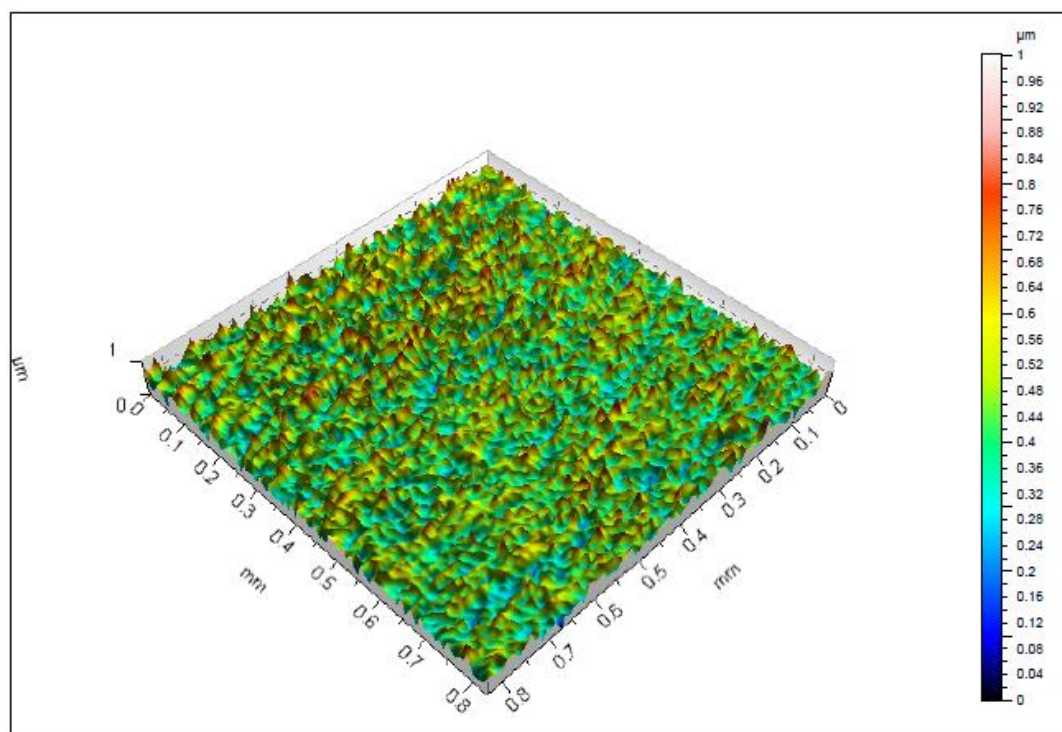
3D vizualizace textury povrchu – soustruženo.
